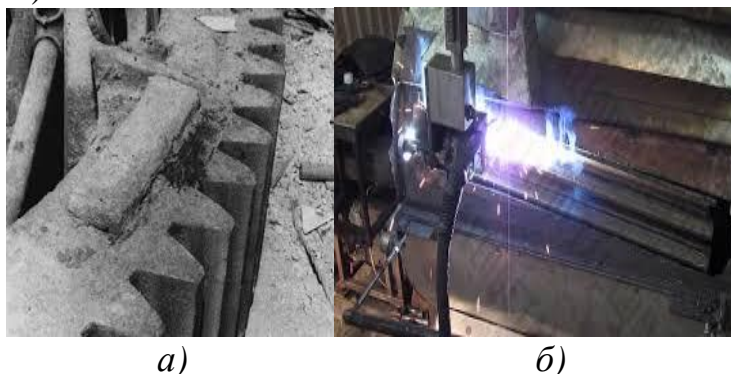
Зношені великогабаритні зубчасті колеса: *a* - ізнощеное циліндричне зубчасте колесо; *б* - наплавлення ізнощеного циліндричного зубчастого колеса
